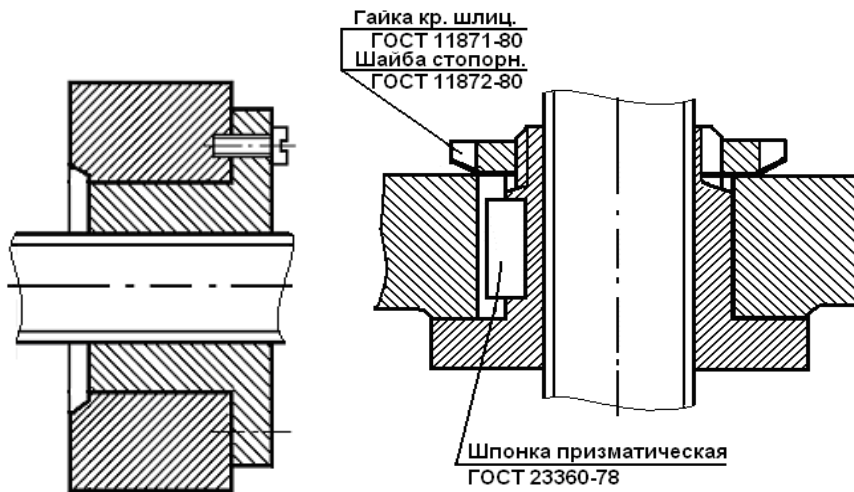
Не вращающаяся гайка, установленная в корпус
